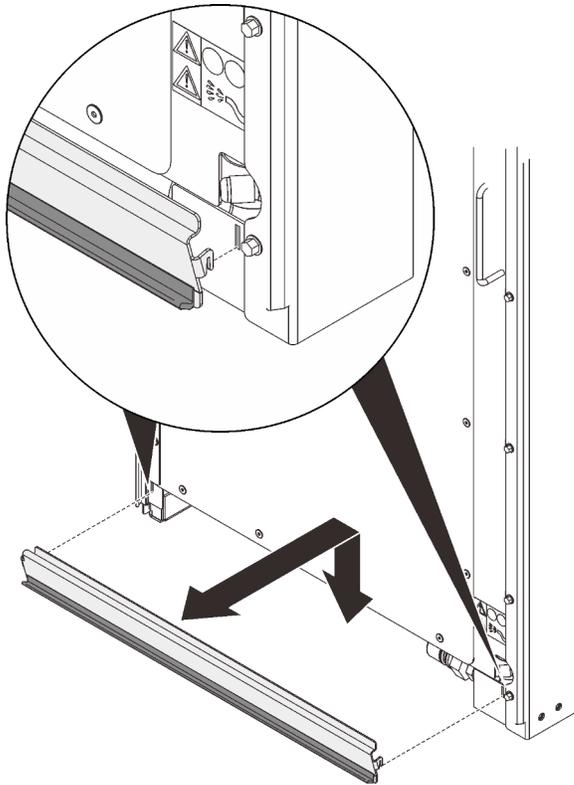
Entfernen der inneren Schlauchzugangsplatte
